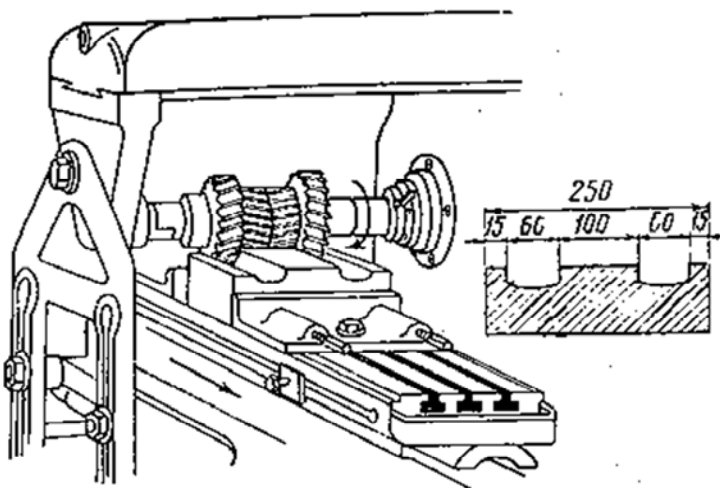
Фрезерование фасонной поверхности набором фрез
